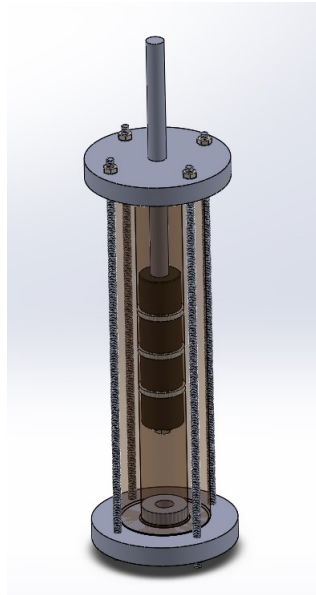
Protótipo final de amortecedor magnético elaborado em SolidWorks
